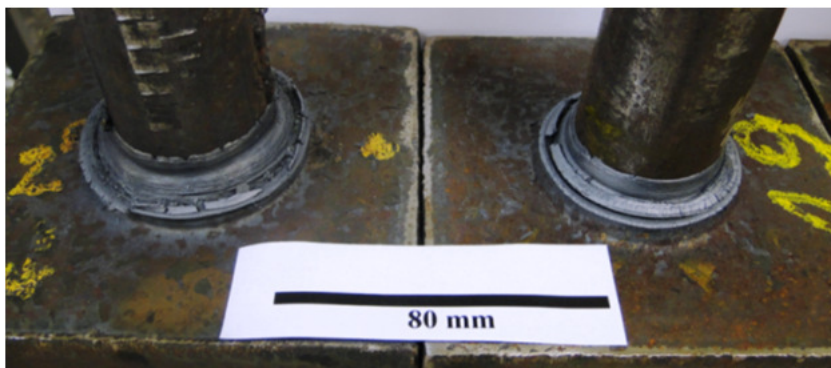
Solda no corpo de prova G03CP18 e G03CP19.
